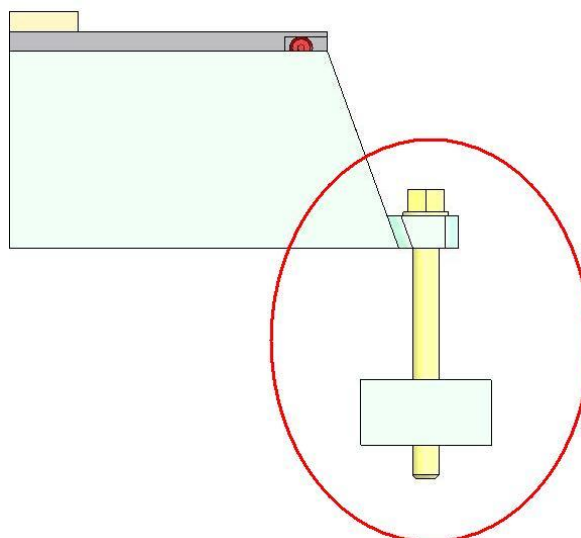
Sistema de fixação da mesa na máquina CNC
